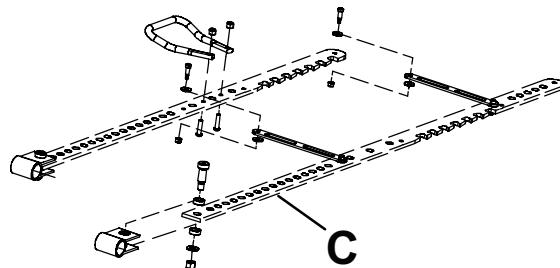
Supports d'ajustement de la hauteur et plaques coulissantes
